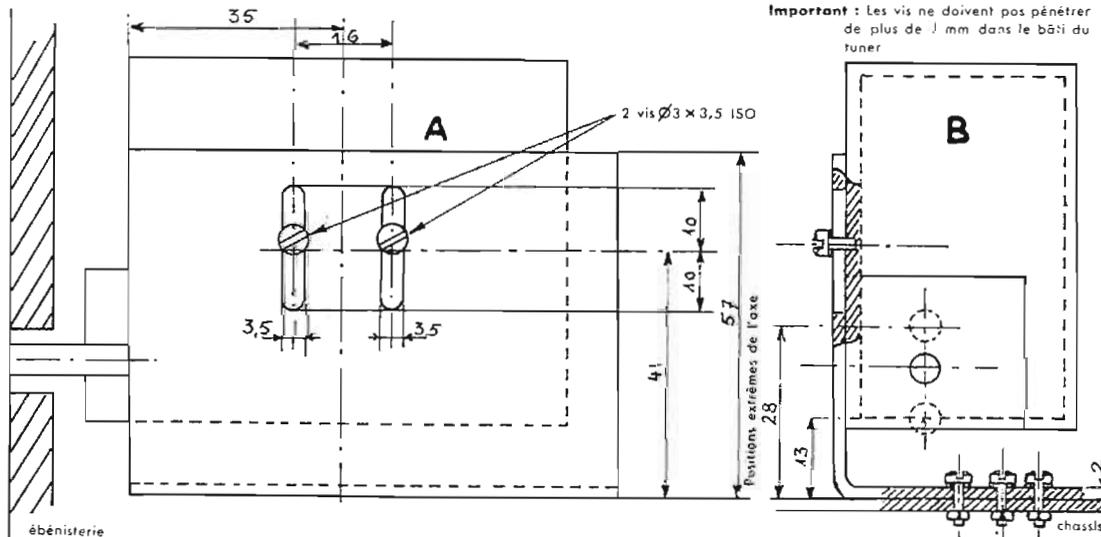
Montage sur la plaquette 4/674. A : vue de côté. B : vue avant.
